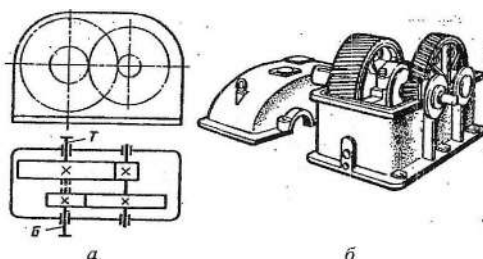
Двухступенчатый горизонтальный редуктор с цилиндрическими колесами
